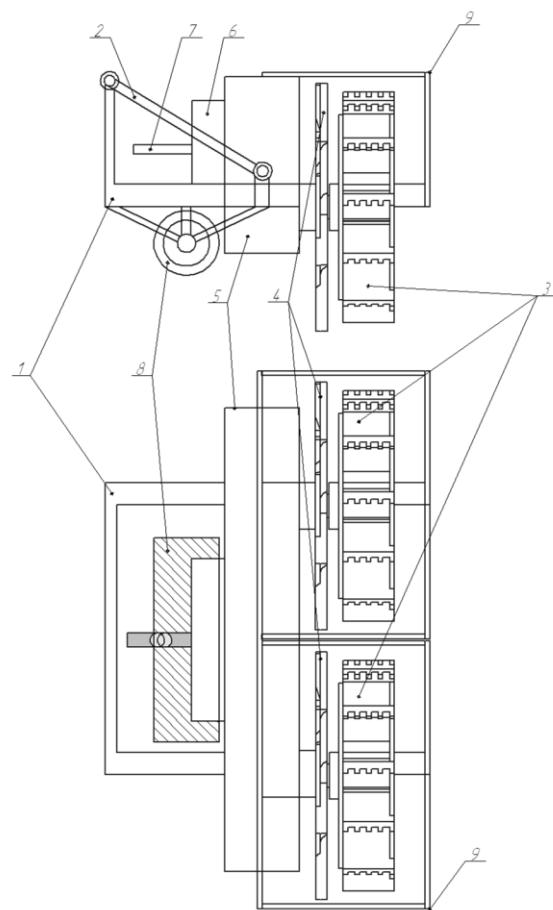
Схема пожарного грунтотема: 1 – несущая рама; 2 – навесное устройство с гидроцилиндром подъема и опускания несущей рамы; 3 – роторные метатели почвы; 4 – роторные фрезы рыхлители почвы; 5 – распределительный редуктор; 6 – муфта предохранительная; 7 – карданный вал; 8 – опорные катки; 9 – направляющие кожухи.
